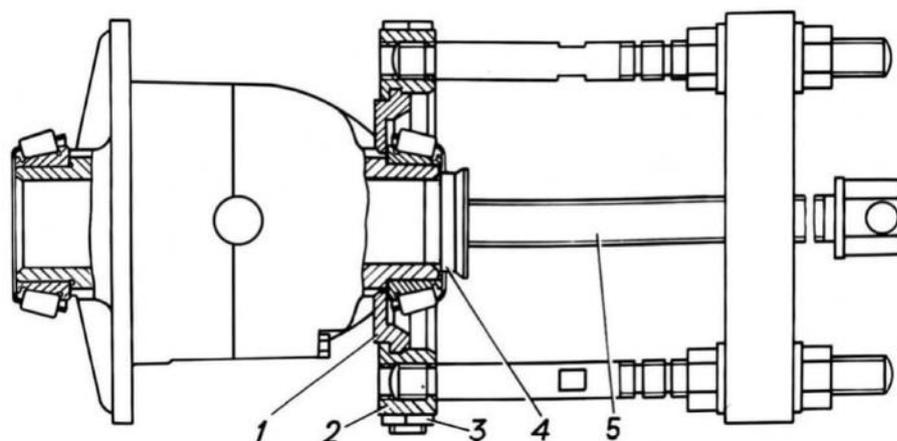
Снятие внутреннего кольца подшипника с коробки дифференциала:
